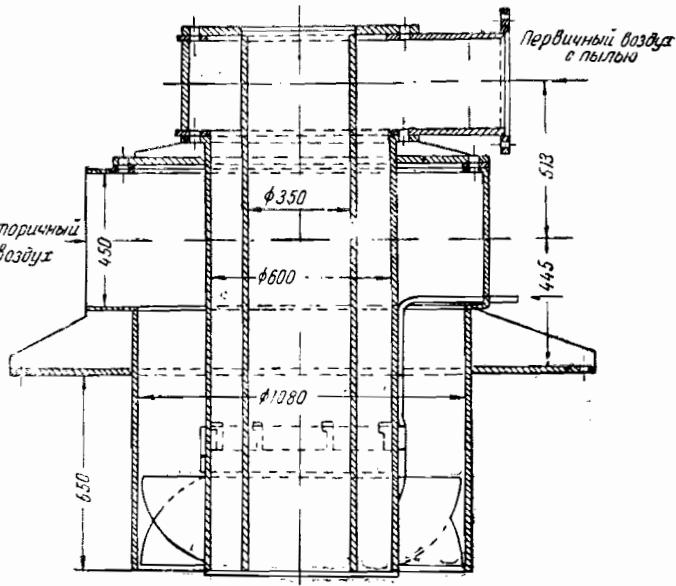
Круглая горелка ВТИ с завихривающими поворотными лопатками
